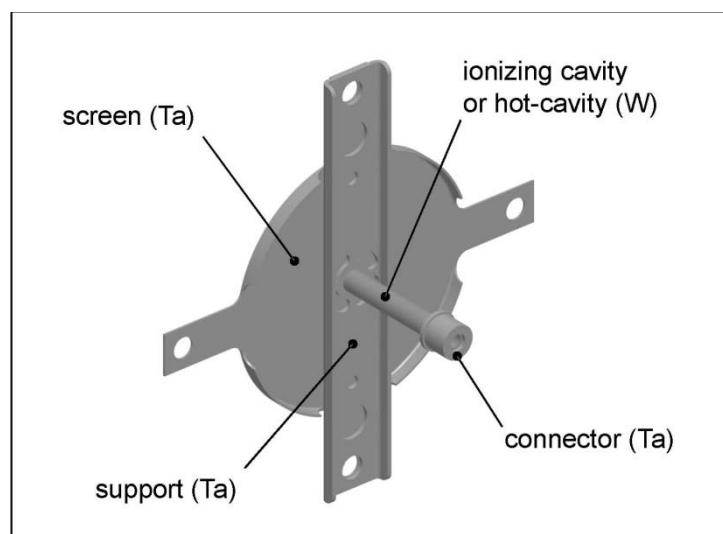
Assemblaggio meccanico della hot-cavity ion source.
